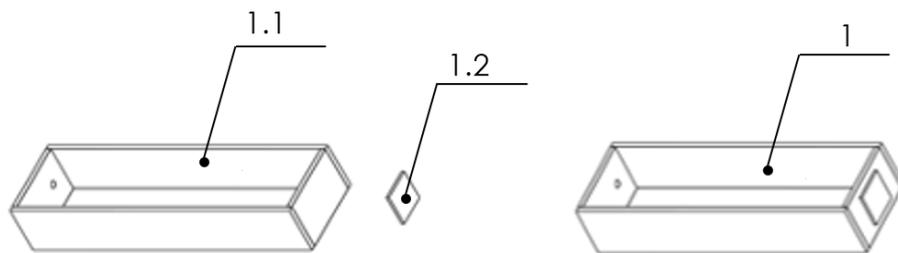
Ensamblaje subconjunto 1 mesa de centro. Filtro adhesivo
